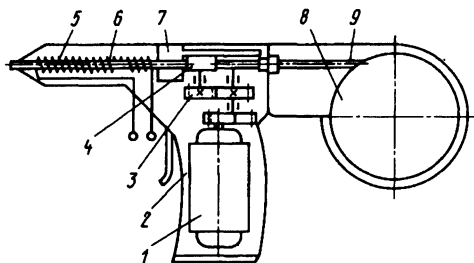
Ручной сварочный инструмент полуавтомата ПСП-5:
